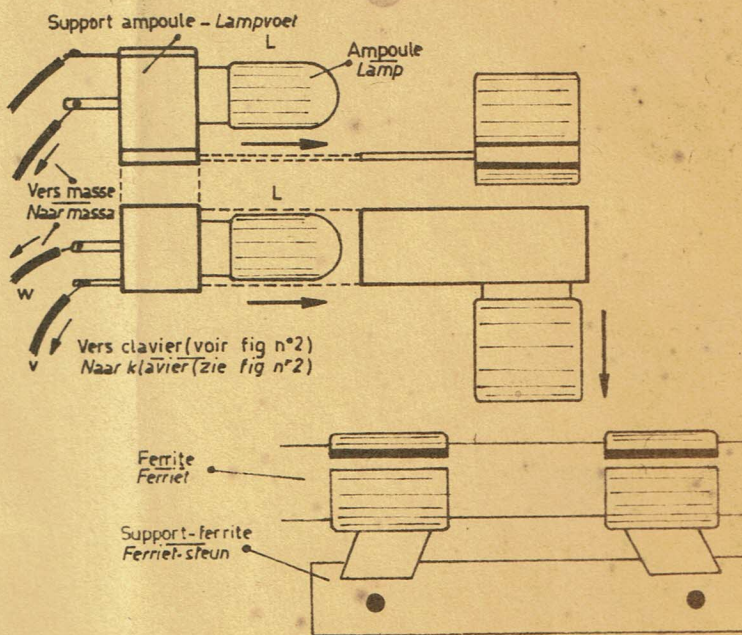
MISE EN PLACE DU SYSTEME
